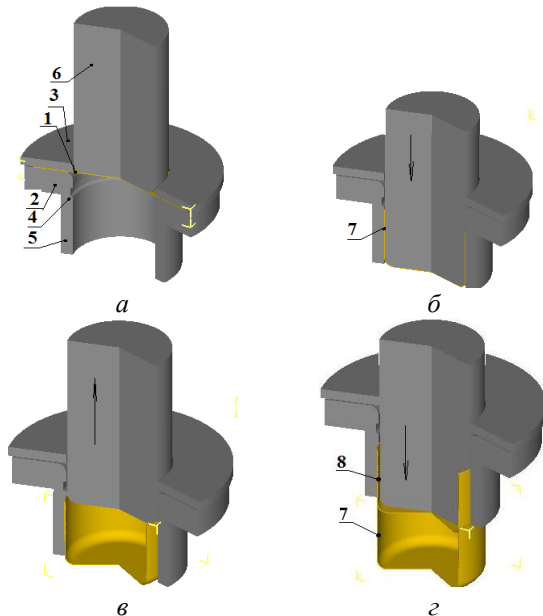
Розрахункові положення в розрізі заготовки і деформуючого інструмента: а – на початку витягування, б – в кінці витягування, в – після знімання виробу з пуансона, г – після виштовхування виробу другою заготовкою
